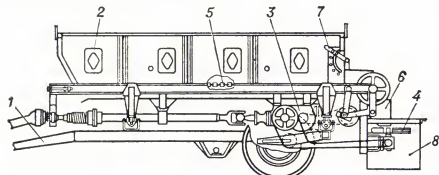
Разбрасыватель минеральных удобрений: 1 — шасси; 2 — кузов; 3 — главный редуктор; 4 — разбрасывающее устройство; 5 — печечно-планчатый транспортер; 6 — топливоделитель; 7 — дозирующее устройство; 8 — ветрозащитное устройство.
